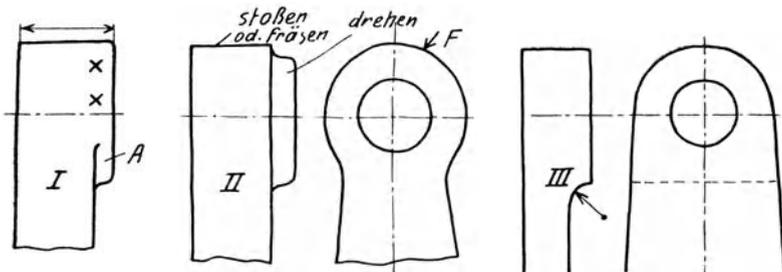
152. Form I für „allseitig“ bearbeitete Kurbeln ungünstig. Form III für gefräste Kurbeln.
